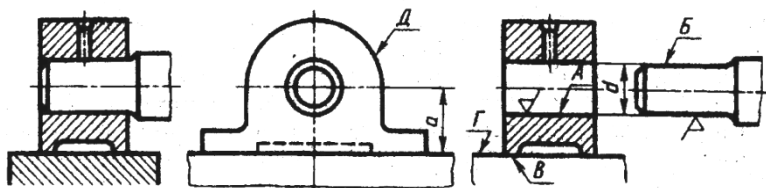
Поверхности деталей: *A, B* – сопрягаемые (*d* – номинальный размер); *B, Г* – привалочные (*a* – координирующий размер); *Д* – свободная
